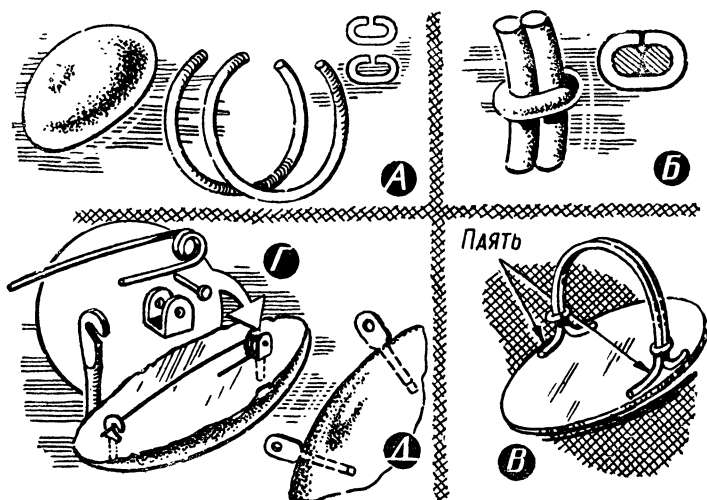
Изготовление перстня: А — заготовки; Б — установка колечек; В — припаивание к основанию; Г — крепление броши и заколки; Д — крепление петельки у кулона.
